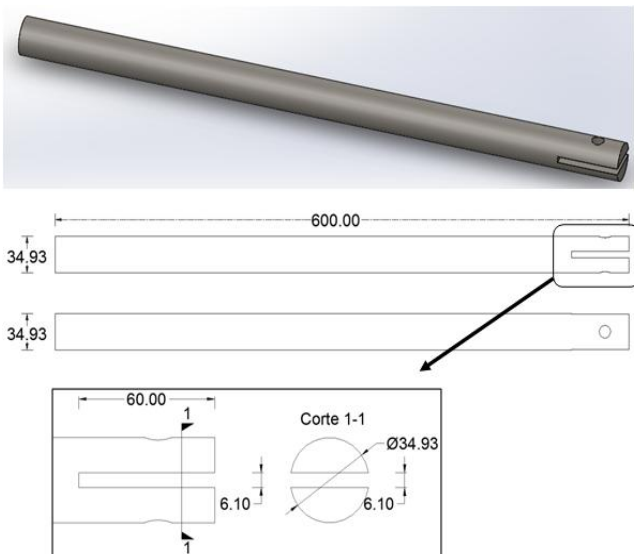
Dimensionamiento y geometría de las barras, cotas en milímetros.
